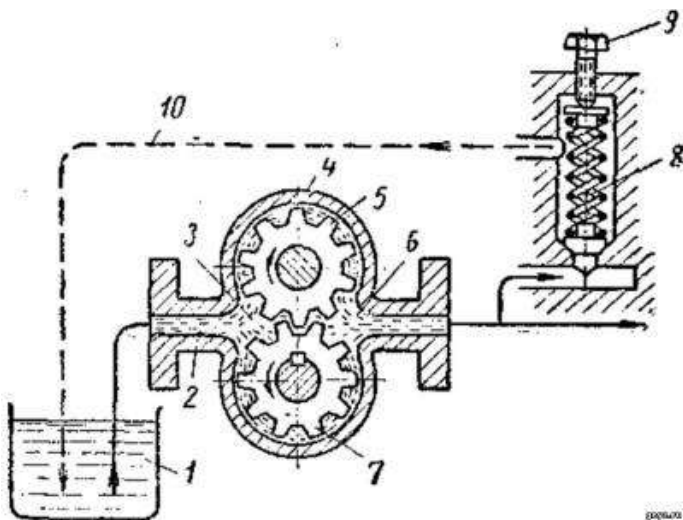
Схема установки шестеренчатого насоса: 1 — масляный бак; 2 — приемный патрубок; 3 — всасывающая полость; 4 — корпус; 5 — ведомая шестерня; 6 — нагнетательная полость; 7 — ведущая шестерня; 8 — перепускной клапан; 9 — регулировочный винт клапана; 10 — сливной маслопровод.
